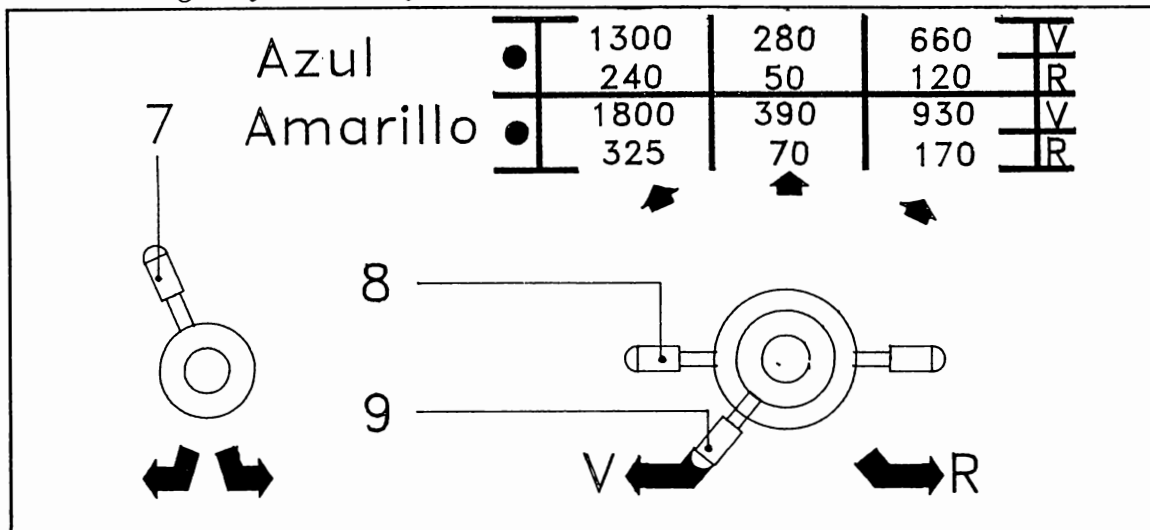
Detalle CABEZAL DEL TORNO.
